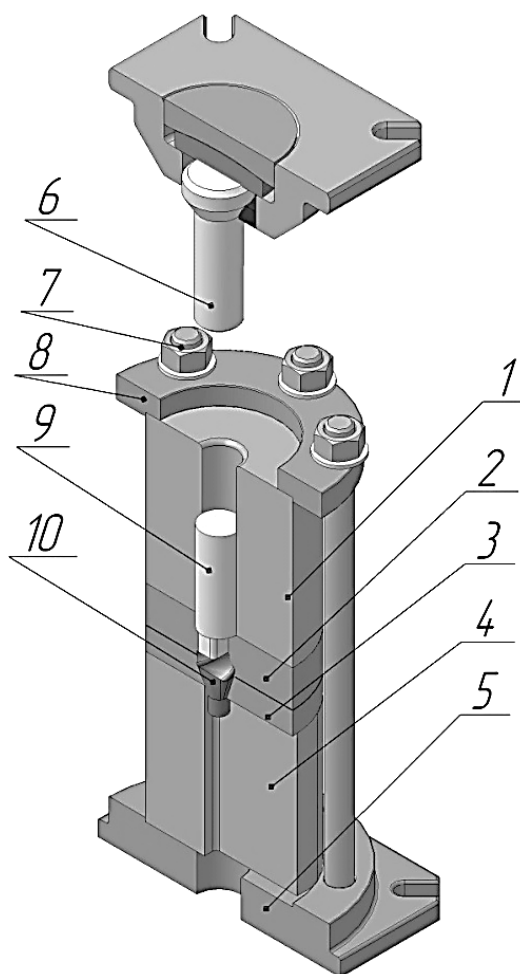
Установка комбинированной экструзии для обработки магниевого порошка
